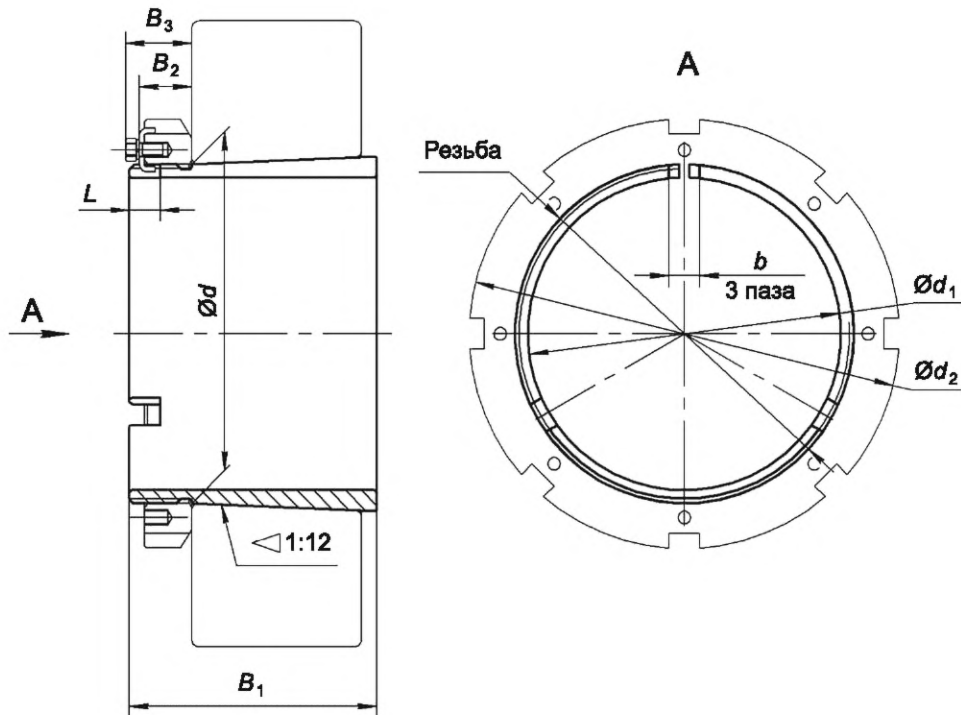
Закрепительная втулка, предназначенная для монтажа подшипника с помощью стопорной гайки, стопорной скобы, стопорного болта и пружинной шайбы
